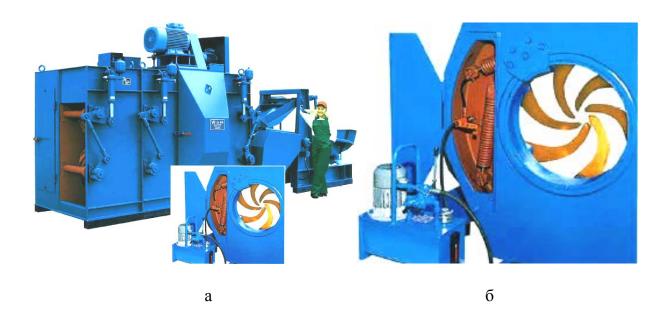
Регулировка давления в гидрофицированном роторе станкаVK26SMX: а – общий вид станка; б – ротор с подключенной гидростанцией
